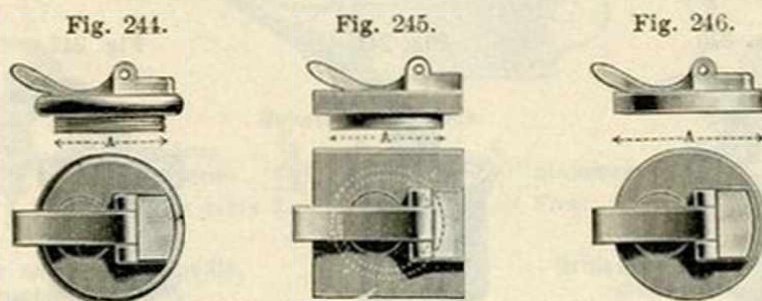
, 245, 246. Couvercles carrés, rectangulaires et ronds, avec ou sans bague.
